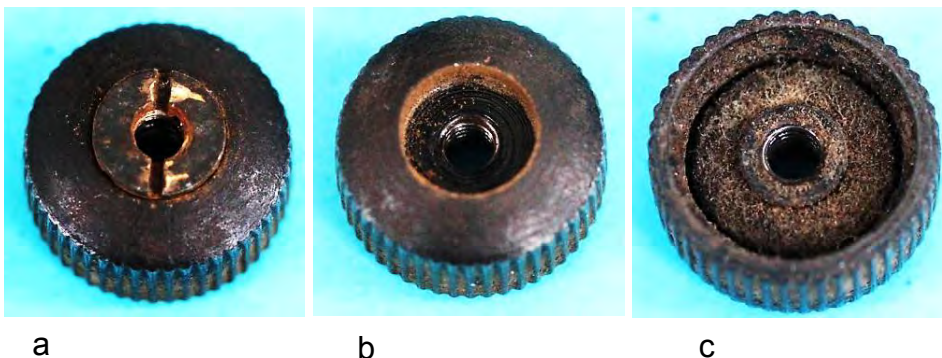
Reibrad: a) Reibrad mit Kontermutter, b) Gewindebohrung im Reibrad, c) Filzring im Innenraum
